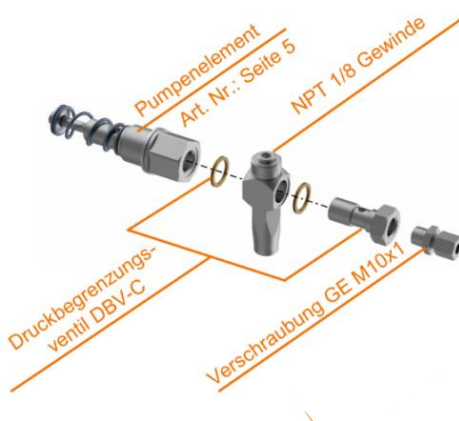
Explosionszeichnung PE mit DBV-C
